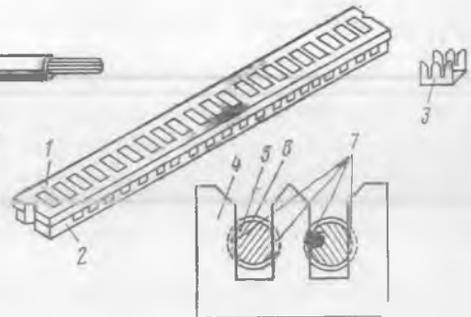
Групповой соединитель СМЖ-10: 1 — крышка; 2 — основание; 3 — клемма; 4 — выступ клеммы; 5 — токопроводящая жила; 6 — изоляция жилы; 7 — места соединения жил с выступами клеммы
